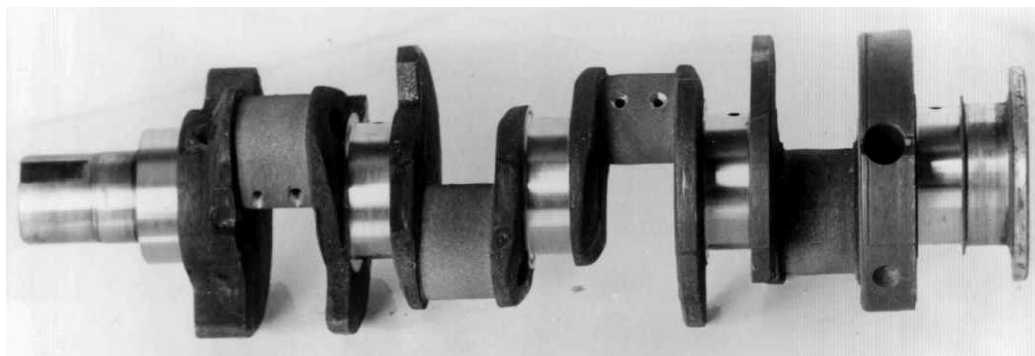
Напилений колінчатий вал з шліфованими корінними шийками
